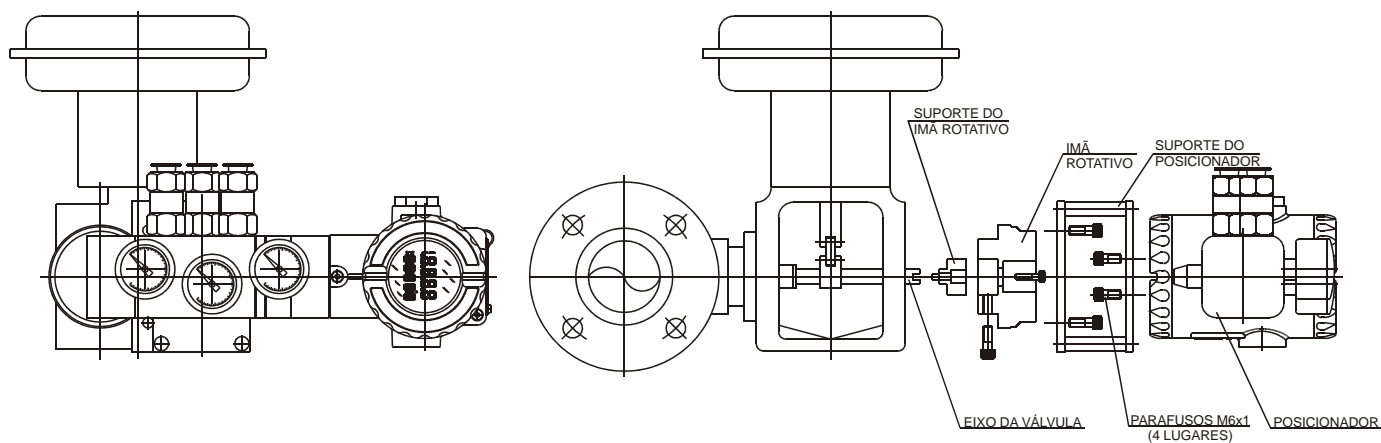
Esquema de Montagem do Posicionador em Atuador Rotativo
